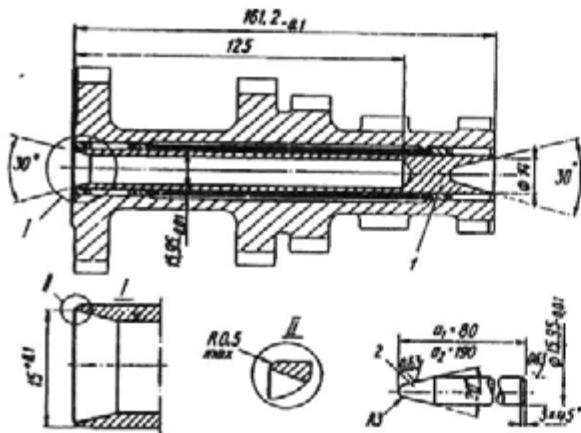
Оправки для выпрессовки и запрессовки оси блока шестерен промежуточного вала:
